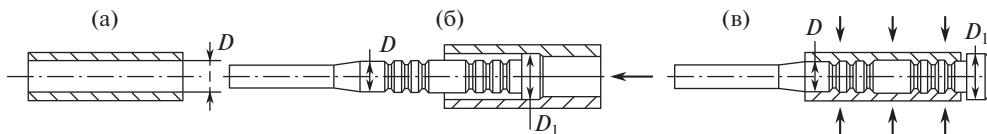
Втулка-заготовка и комбинированная прошивка а – втулка-заготовка с гладким цилиндрическим каналом,  $D$  – диаметр втулки; б – комбинированная прошивка, формирующая внутренний профиль муфты,  $D_1$  – диаметр дорна,  $L_{\text{общ}}$  – общая длина прошивки,  $L$  – длина рабочей части прошивки.
